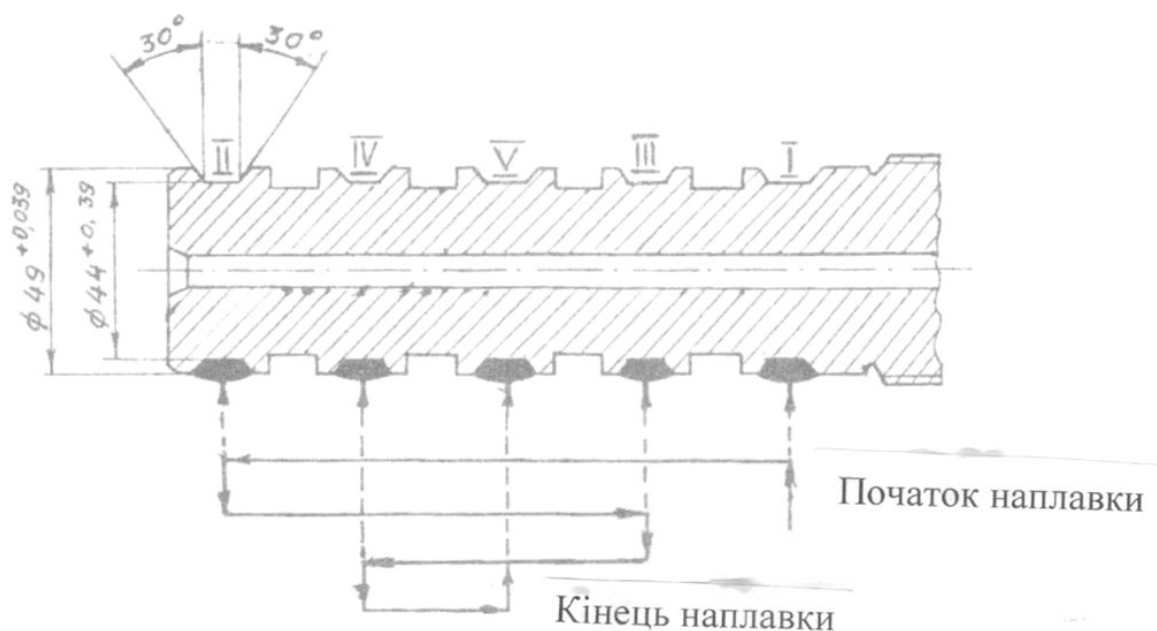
Схема підготовки та наплавлення канавок вторинного валу 150.37.037-2 коробки передач
